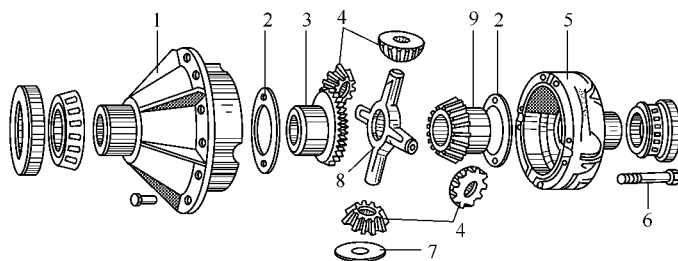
载质量 3t 和 3t 以上车的差速器零件图
